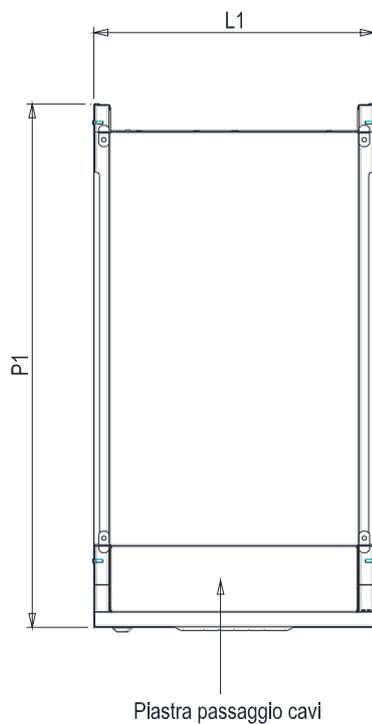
Pianta di base armadio batteria esterno Tipo 2
